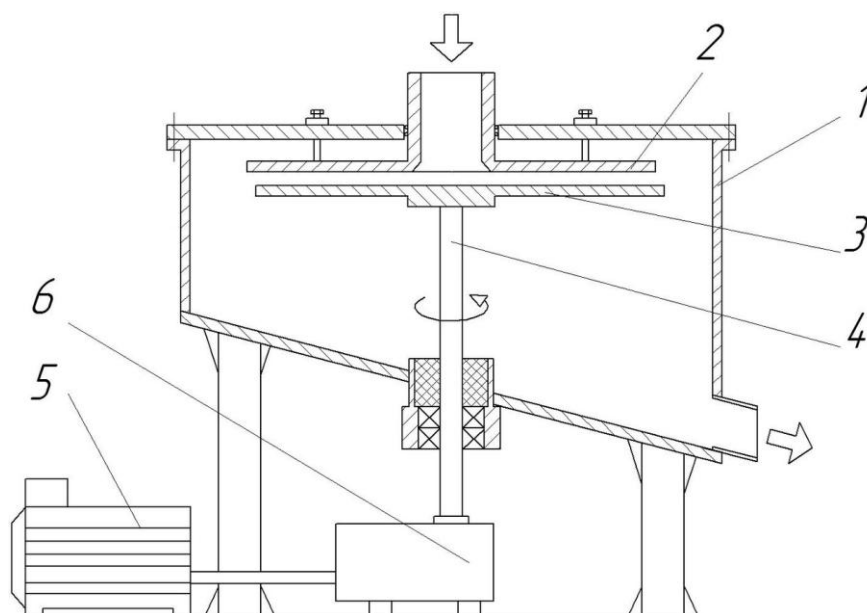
Схема лабораторного млина: 1 – корпус; 2 – нерухомий диск; 3 – рухомий диск; 4 – приводний вал; 5 – електродвигун; 6 – редуктор
